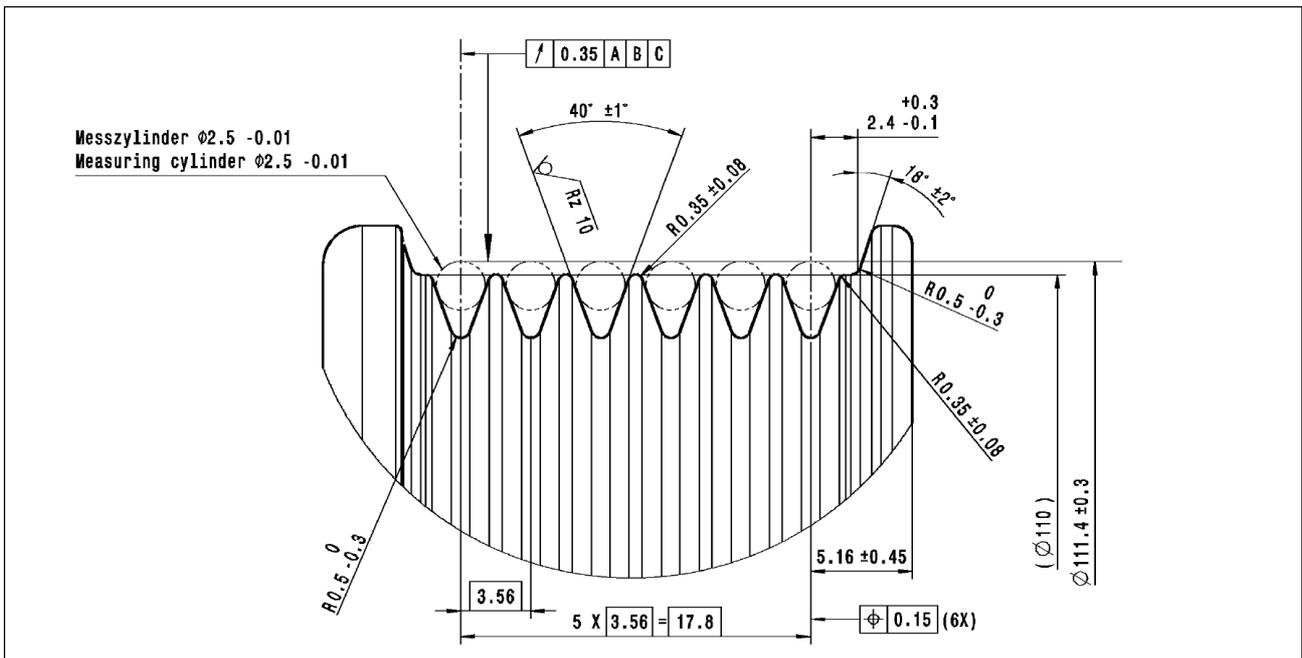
Детальное изображение U – шкив компрессора климатической установки Denso 6SES14, диаметр шкива d=110 мм
